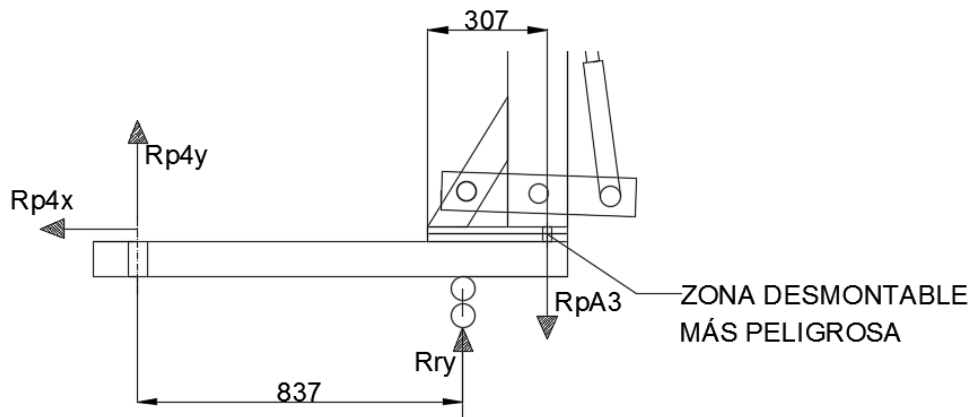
Vista de la sección desmontable más peligrosa sometida a cargas de tracción. Fuente: Elaboración Propia
